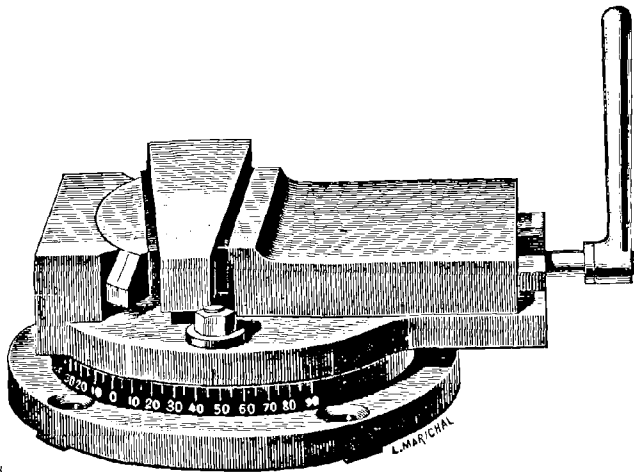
Etau à base tournante graduée et serrage automatique des pièces obliques.
